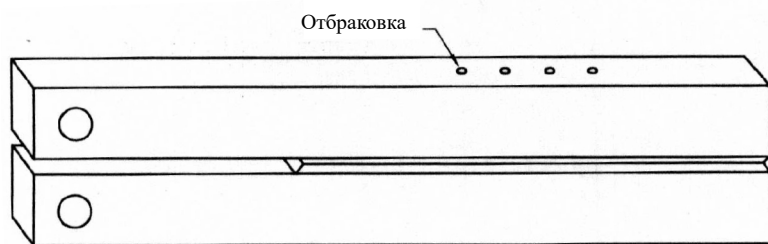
Расположение отпечатков при определении твердости на образце DCB
